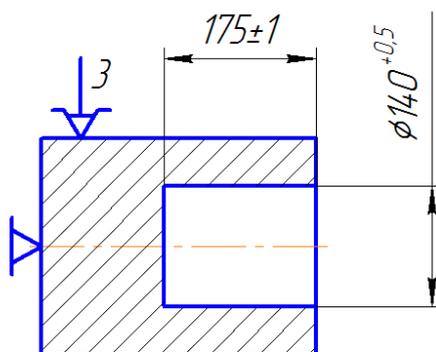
Эскиз базирования заготовки на 005 токарной операции.
